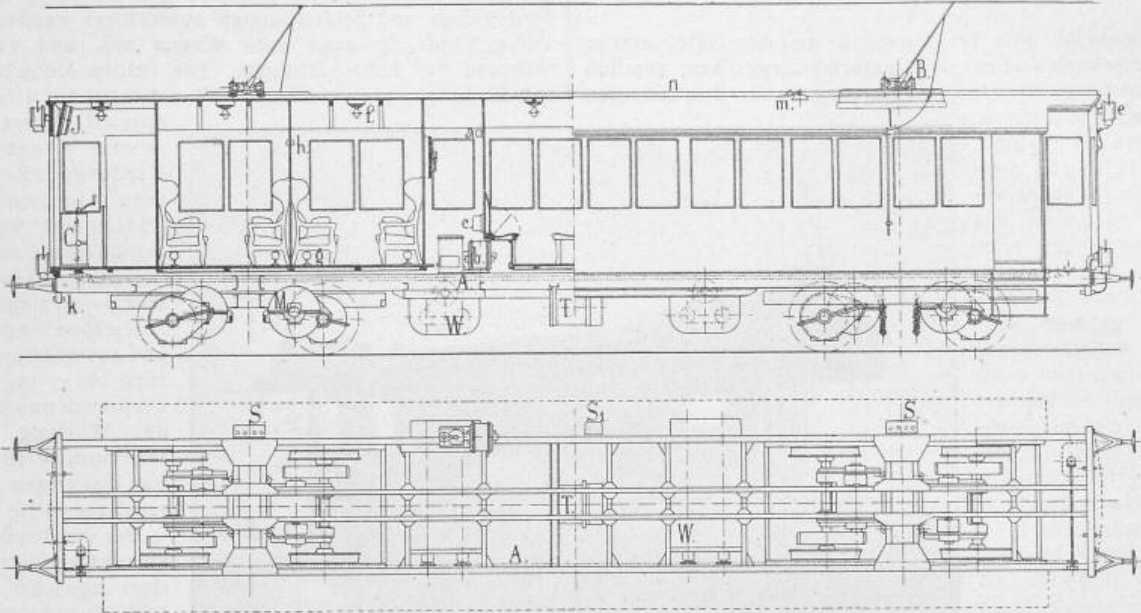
Ansicht und Grundriss. 1:100.
